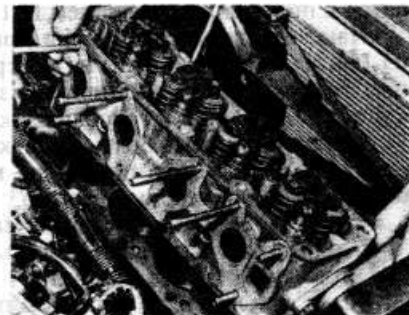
Отделение головки от блока цилиндров — двигатель 1,6 л с многоточечным впрыском топлива
